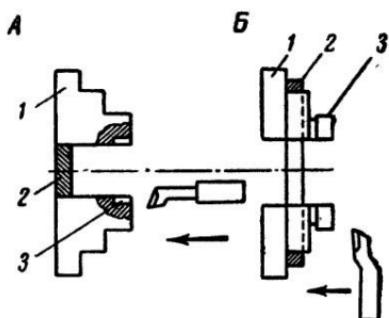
Обработка сырых кулачков: A — для закрепления детали за наружный диаметр; B — для закрепления детали за отверстие (1 — кулачок, 2 — вспомогательная деталь, 3 — обработанное посадочное место для обрабатываемой детали).
